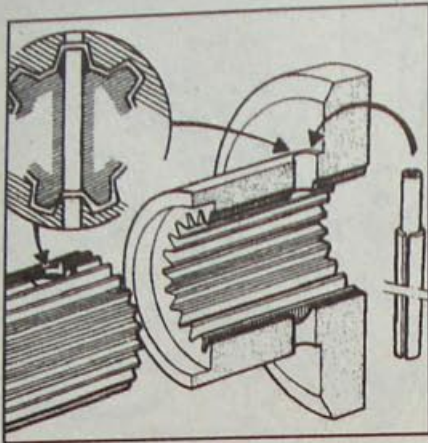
Совмещение отверстий в приводном валу и полуосевой шестерне для установки упругого штифта
